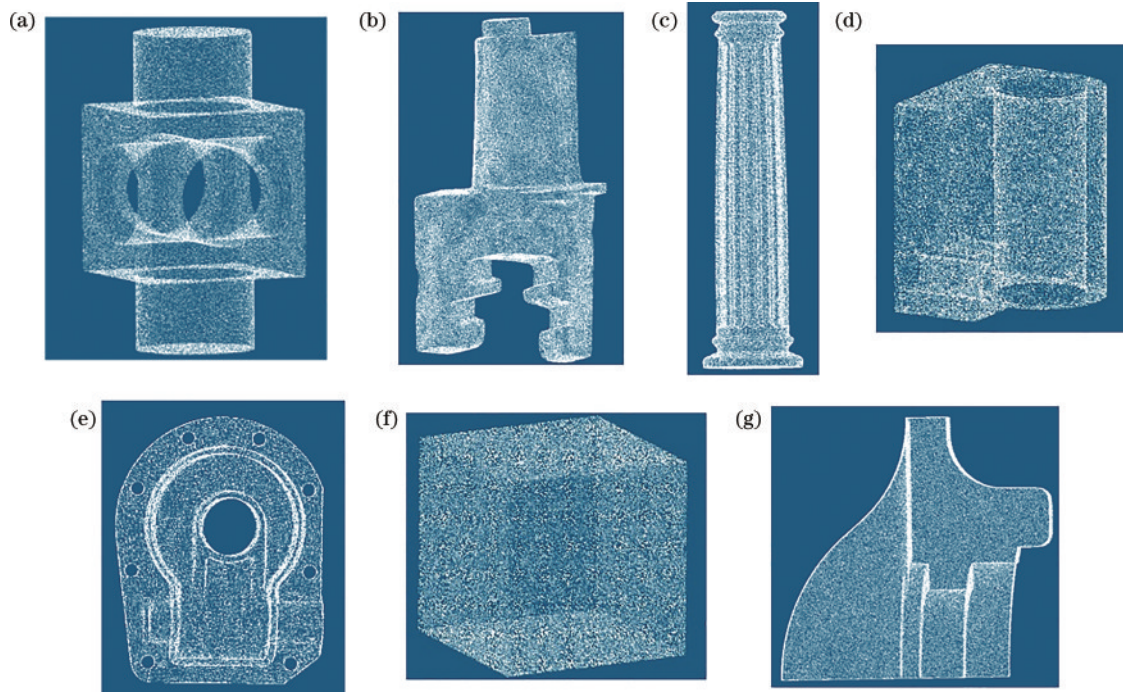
点云数据集。(a) block; (b) blade; (c) column; (d) joint; (e) casting; (f) cube; (g) fandisk
